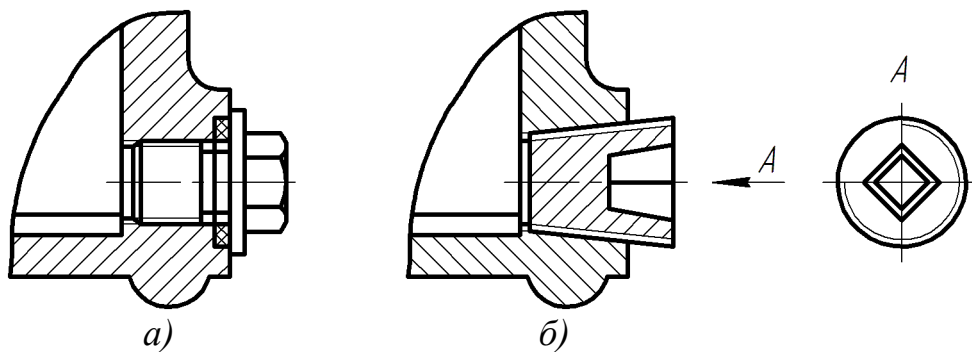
Зливний отвір з пробкою з циліндричною а) та конічною б) нарізками
